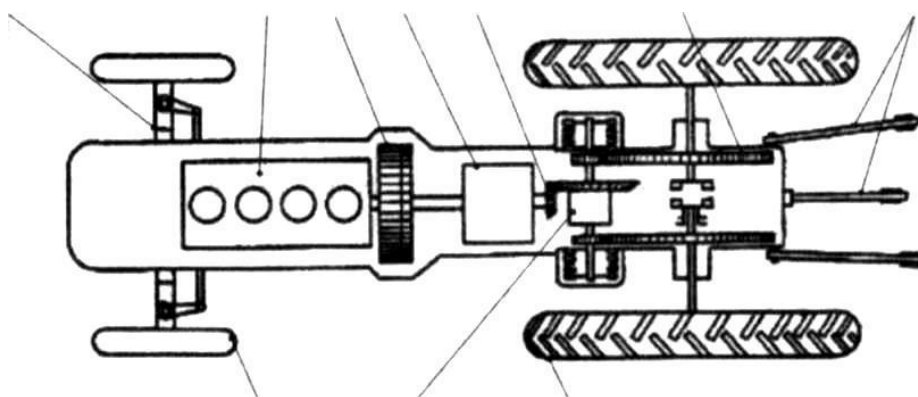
Схема расположения основных агрегатов и узлов колесного трактора:
